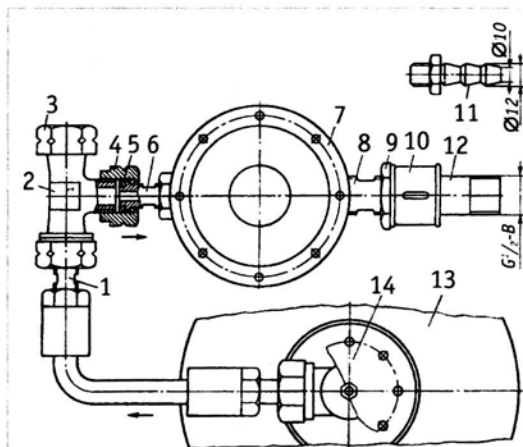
Регулятор давления газа РДГ-8: 1 — присоединительная трубка в сборе; 2 — тройник; 3 — заглушка; 4 — накидная гайка регулятора с левой резьбой; 5 — прокладка; 6 — входной штуцер; 7 — корпус регулятора; 8 — выпускной штуцер; 9 — контргайка; 10 — муфта; 11 — вариант выпускного штуцера для рукава; 12 — боценок (конец трубы); 13 — баллон; 14 — угловой вентиль
